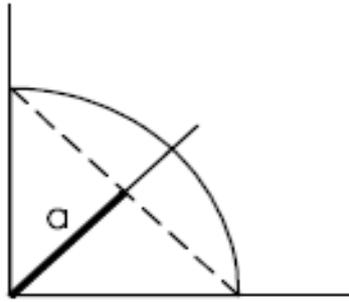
Triángulo isósceles que define el cordón de soldadura.
